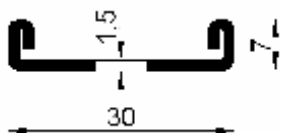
Coupe du rail de fixation Sarnabar® 6/10
